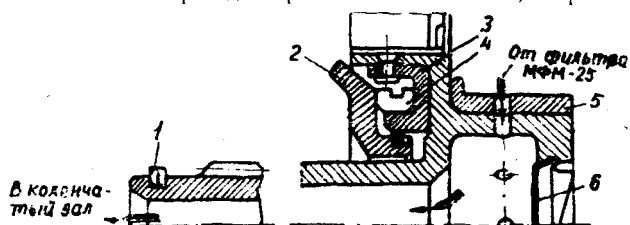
Вал привода агрегатов (продольный разрез): 1—маслоуплотнительные кольца; 2—пята нагнетателя; 3—втулка; 4—упорное кольцо; 5—втулка; 6—заглушка
